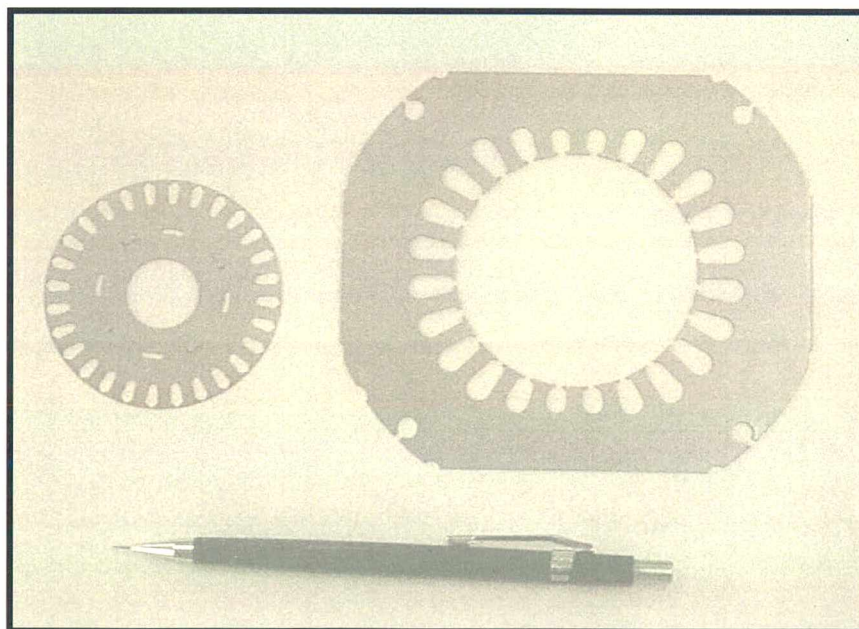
Conjunto de lâminas do motor para compressor; rotor (esquerda) e estator (direita).
